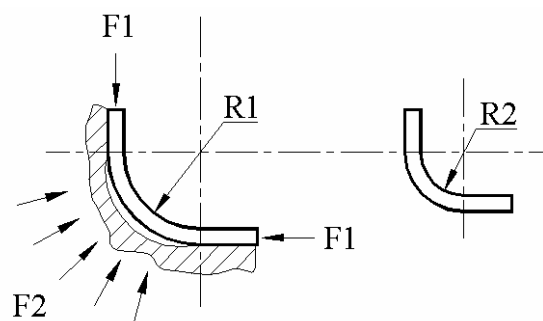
Формовка уголковых зон профиля с приложением тангенциальных сил
